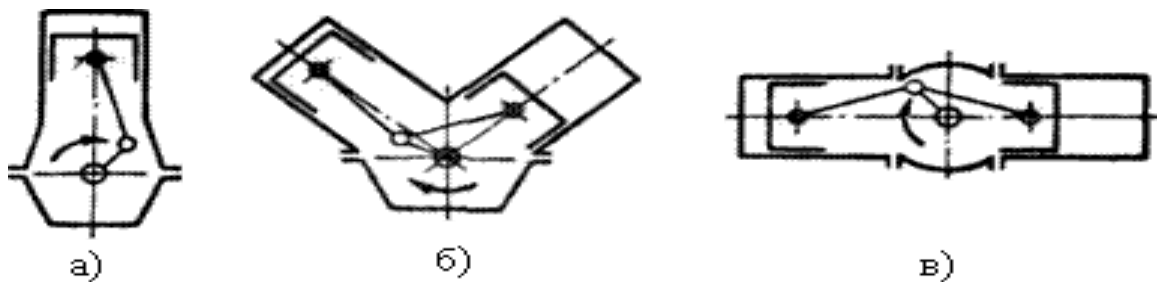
Схеми розміщення циліндрів багаточиліндрового двигуна: а – вертикальне однорядне;
